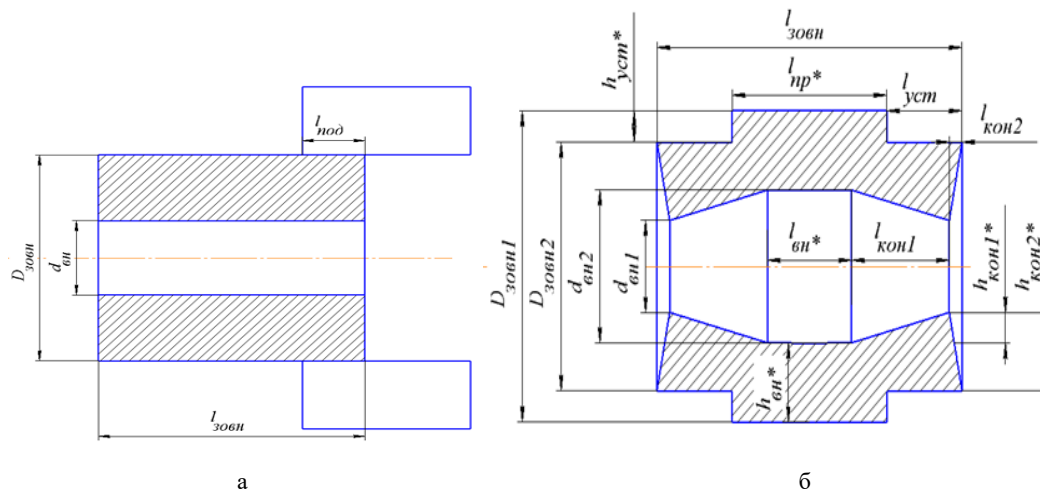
Заготовка до початку кування (а), кована поковка (б)
